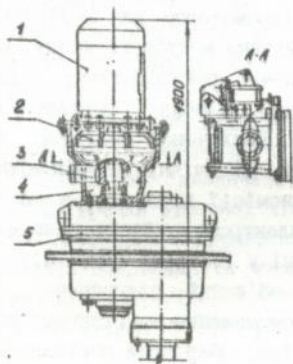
Гідродинамічний привод механізму обертання крану: 1-електродвигун; 2-гідромуфта; 3-гальмо; 4-кронштейн; 5-редуктор
